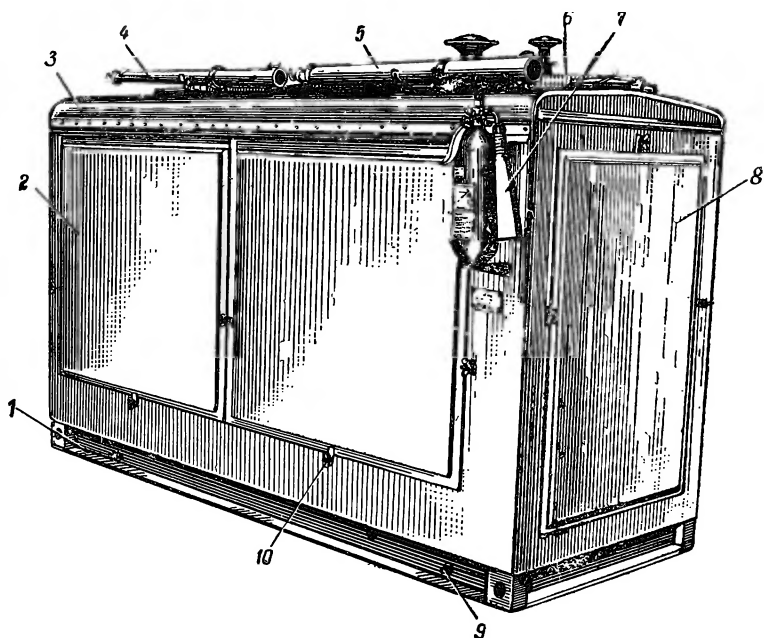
Общий вид агрегата АД-20 с капотом и закрытыми дверцами:
